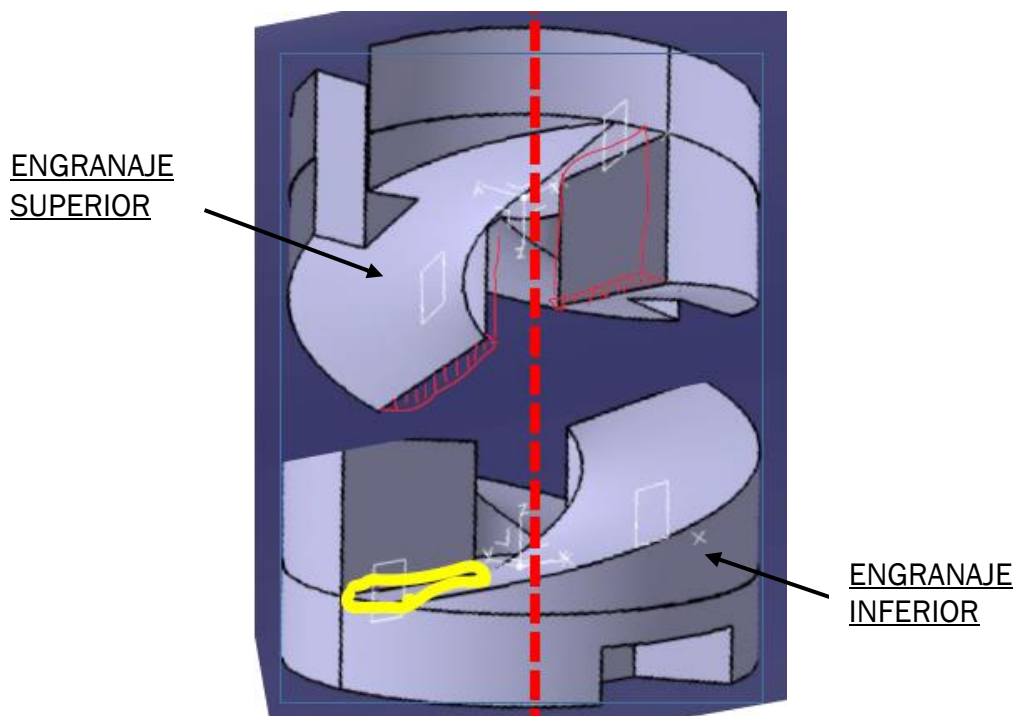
Zona de impacto entre el engranaje superior y el engranaje inferior.
